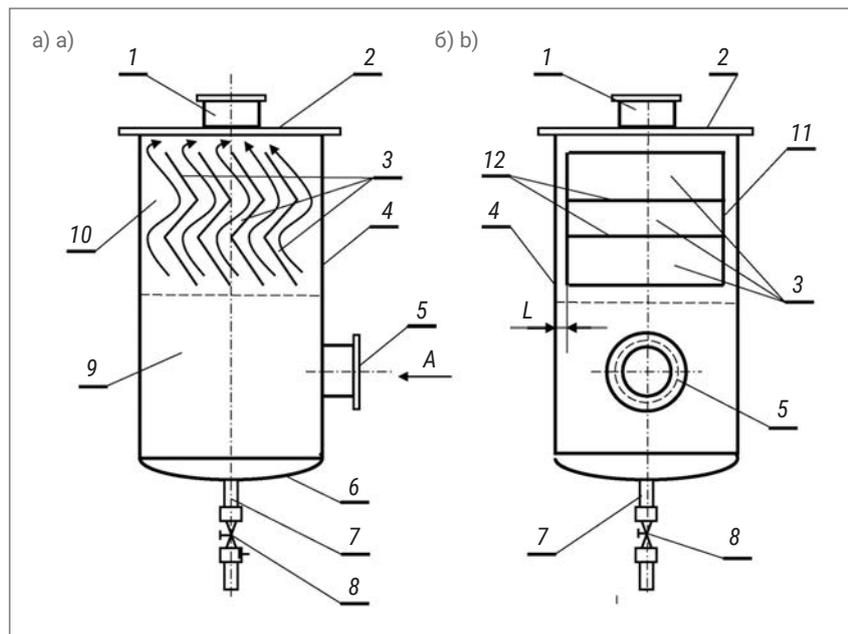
Фильтр-грязевик для очистки жидких сред: а) вид спереди; б) вид сбоку по линии А: 1 – выходной патрубок; 2 – крышка; 3 – блок горизонтально расположенных гофрированных поверхностей; 4 – корпус; 5 – входной патрубок; 6 – выпуклое дно корпуса; 7 – патрубок; 8 – кран для дренирования и продувки нижней части корпуса и вывода осевших примесей из корпуса; 9 – нижняя половина корпуса с первой ступенью очистки; 10 – верхняя часть корпуса со второй ступенью очистки; 11 – боковая сторона; 12 – линии изгиба горизонтально расположенных гофрированных поверхностей. Расстояние между каждой боковой стороной каждой гофрированной поверхности и внутренней стенкой корпуса выполнено равным от 0,05 до 0,10 диаметра корпуса [3]
